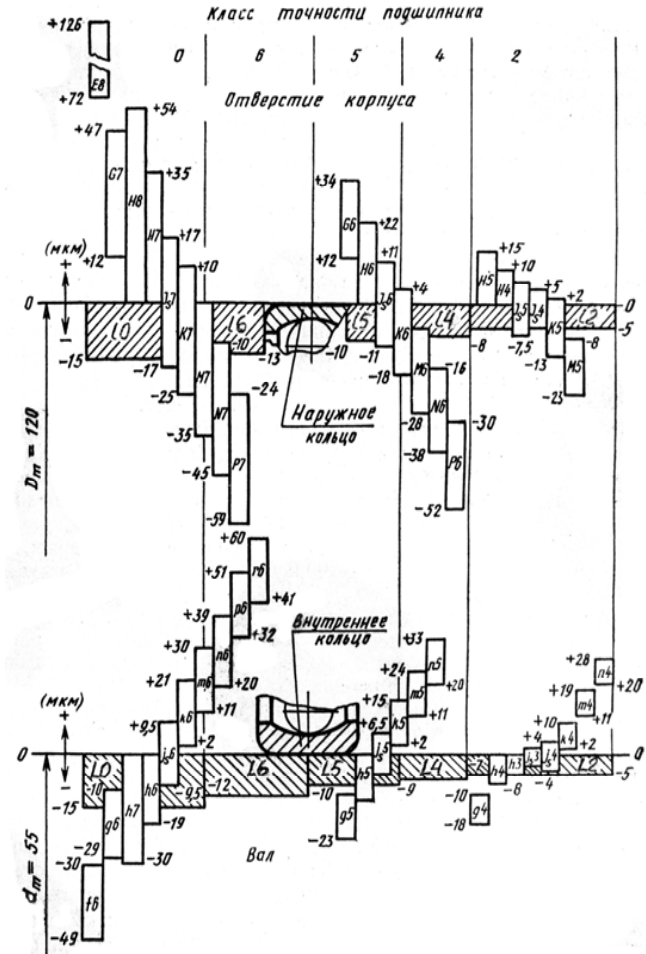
Схемы расположения полей допусков на диаметры колец подшипников качения (KB – внутреннего; hB – наружного), отверстий в корпусах и валов (отклонения в мкм)
